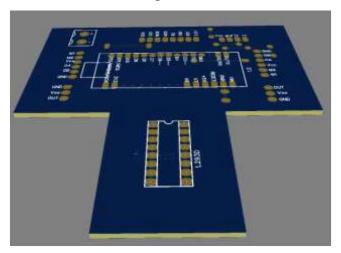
Modelo en 3D de la PCB del prototipo. Elaboración: El autor.
